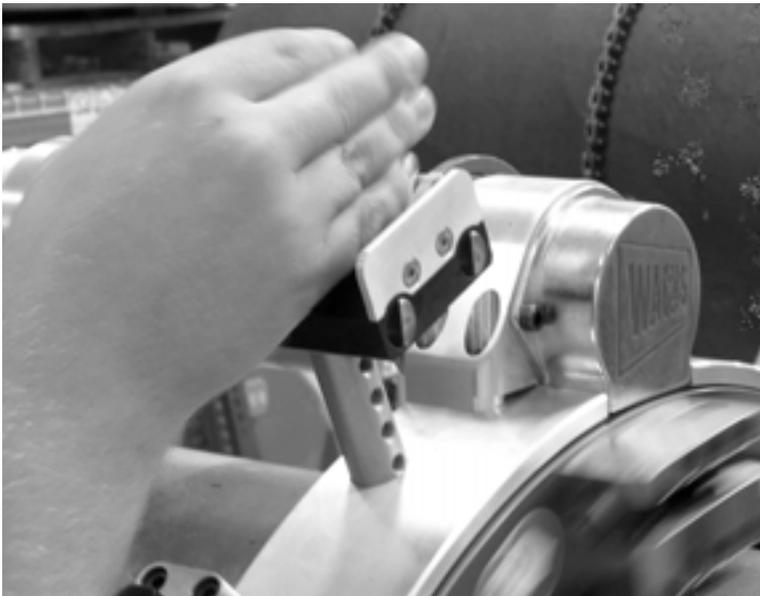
Drücken Sie die Auslöserknöpfe zurück, um die Auslöser vor dem Maschinenstart zu deaktivieren.
